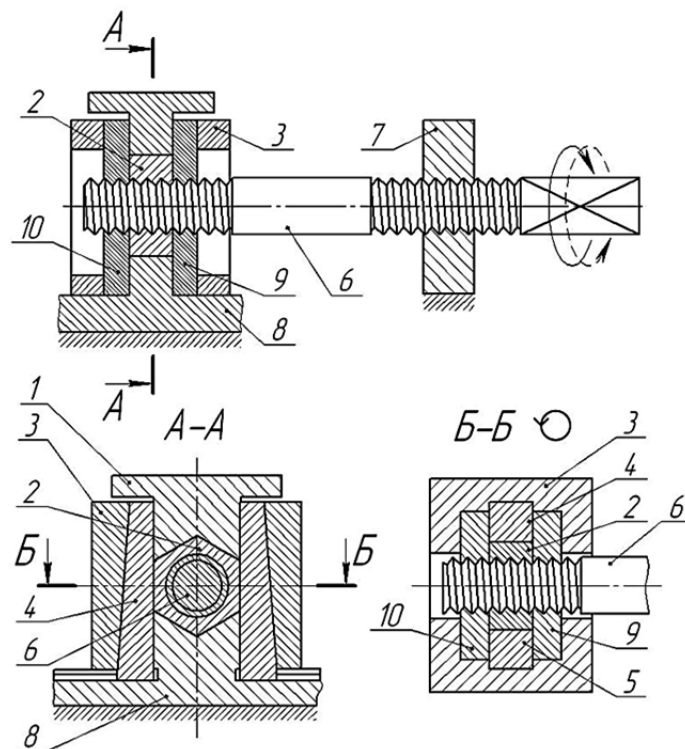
Схема устройства для выдавливания резьбы на гайках
